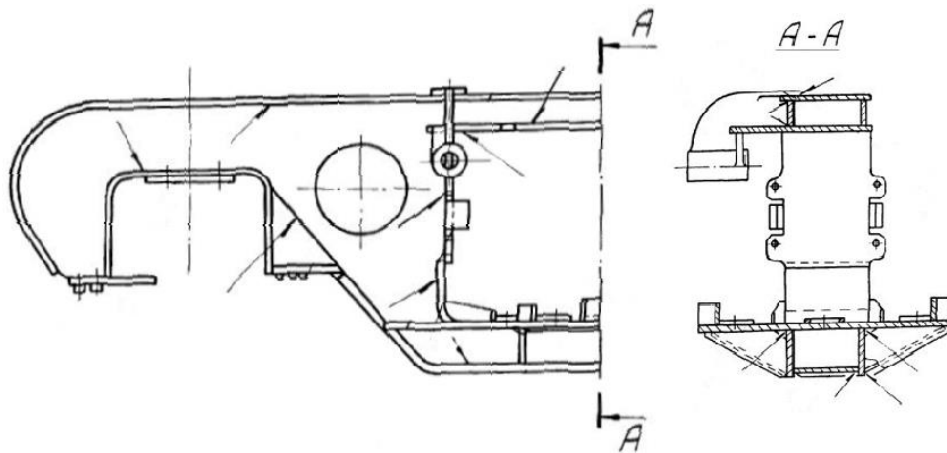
Зварна конструкція бокової рами візка, розробник КВБЗ
